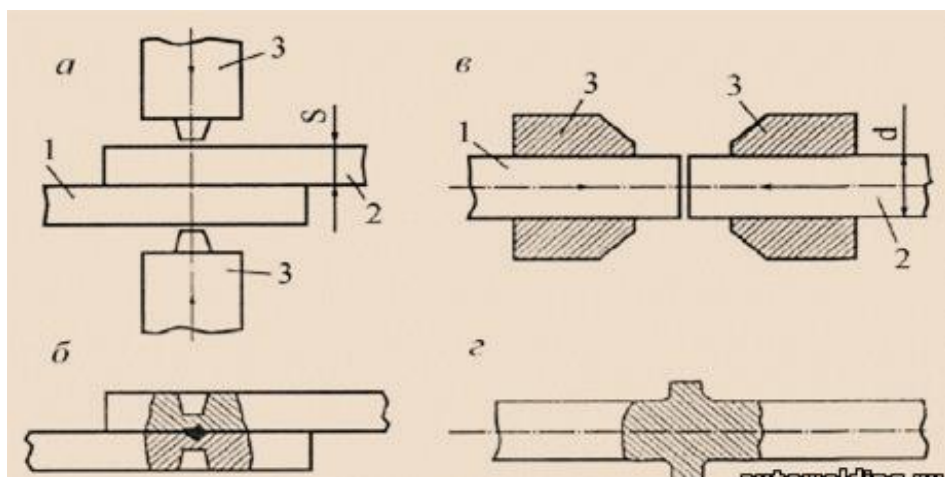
Схемы холодной сварки усилиями, нормальными к поверхности соединения:
